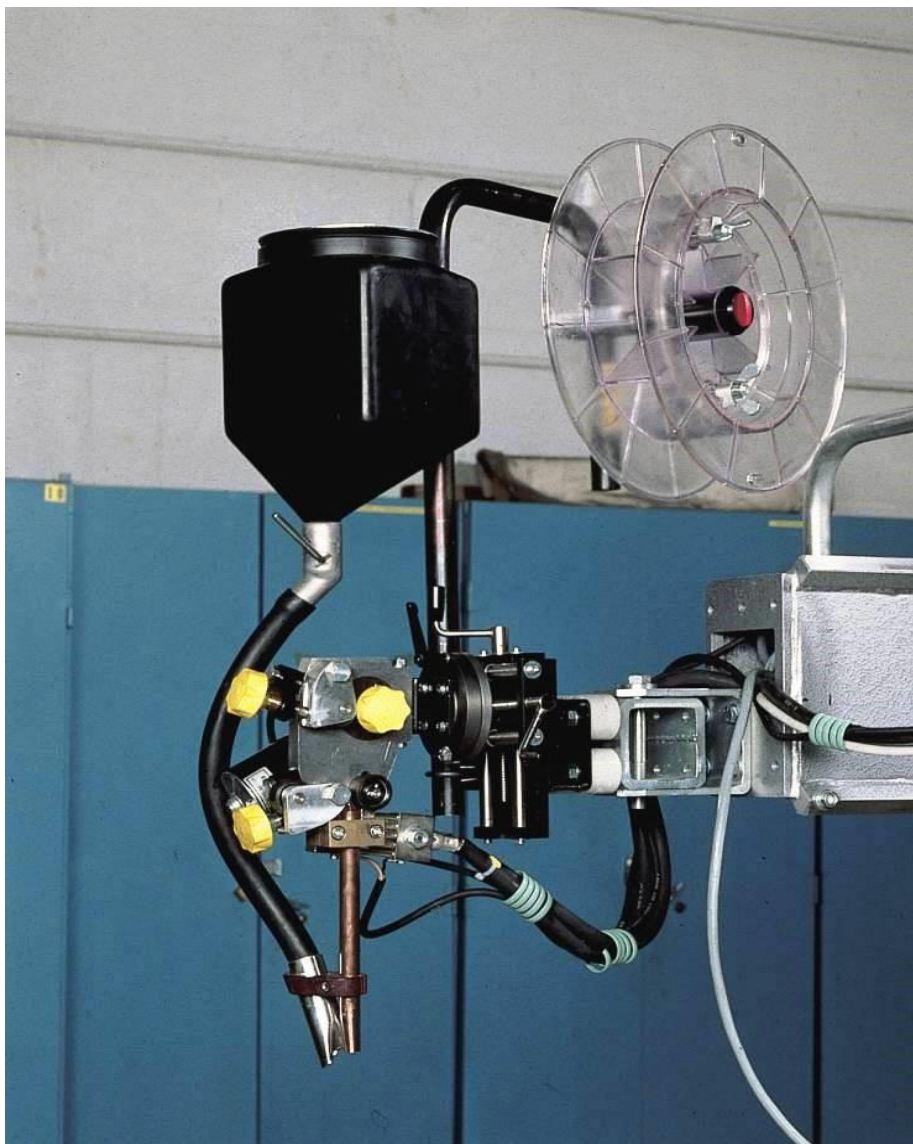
Головка марки ESAB A2 MINI MASTER
